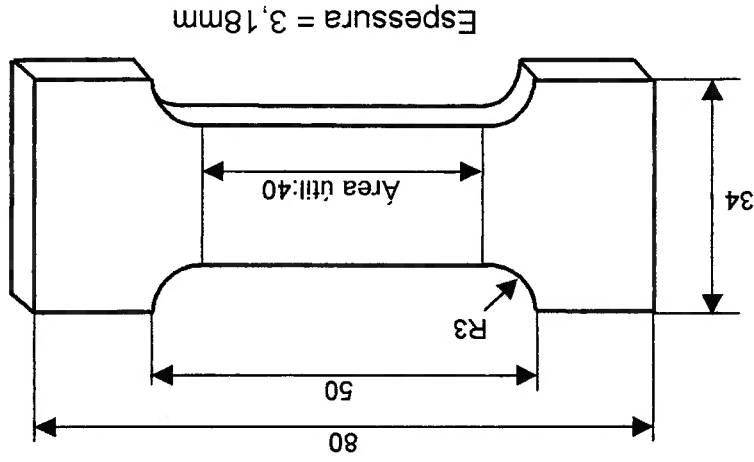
Corpo de Prova para Ensaio de Tração (Unidade:mm)
